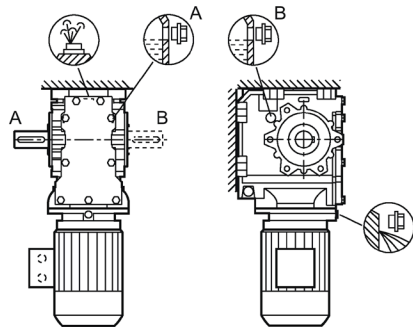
Einbaulagen für Stirnrad Schneckengetriebe C. Fußausführung Baugröße 29
